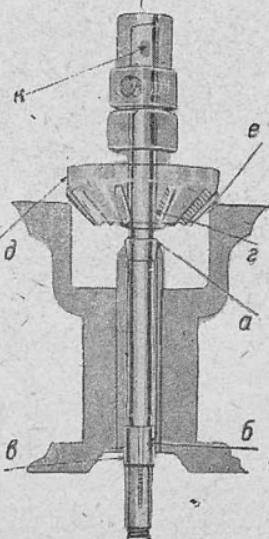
Зубчатая фреза для снятия нагара с клапанных гнезд
